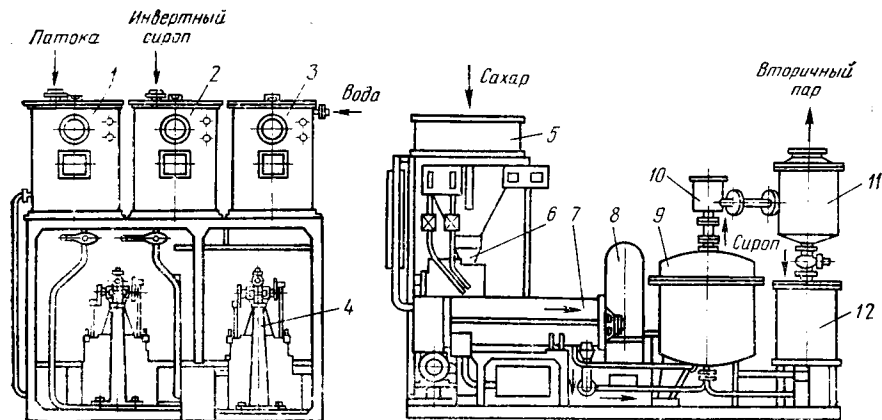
Схема сироповарочного агрегата для приготовления карамельного сиропа под давлением.
